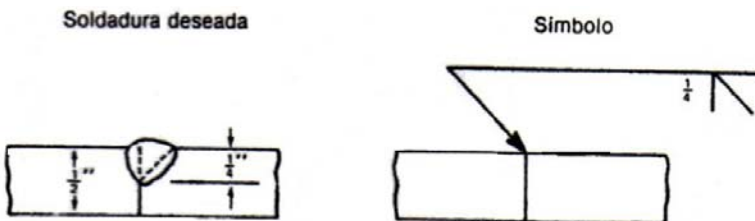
Símbolo de soldadura en el que se especifica la profundidad de la soldadura de ranura.
